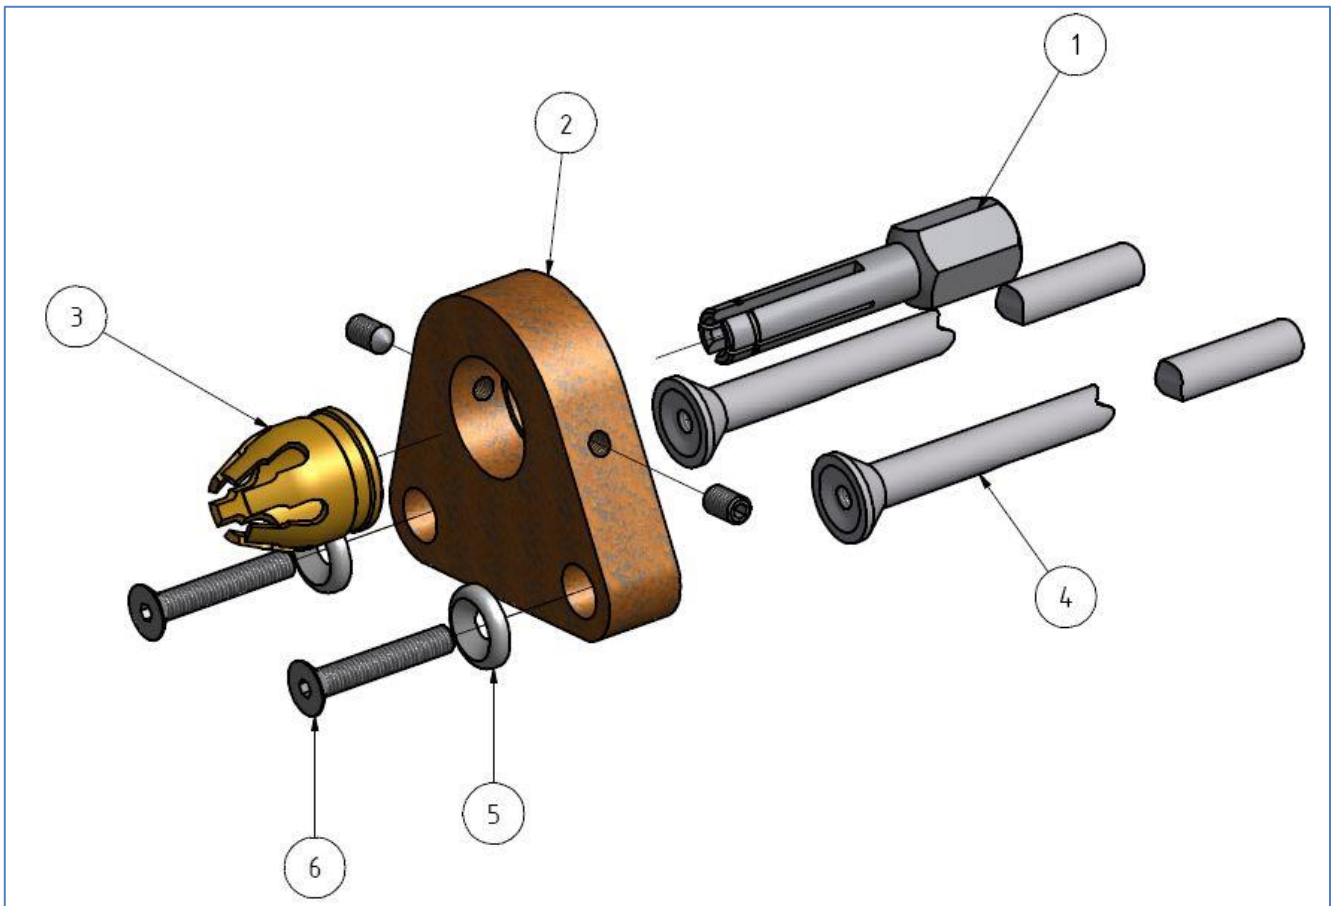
Stützeinrichtung zum Schweißen von Faserfix-Stiften Ø 5, Länge L
